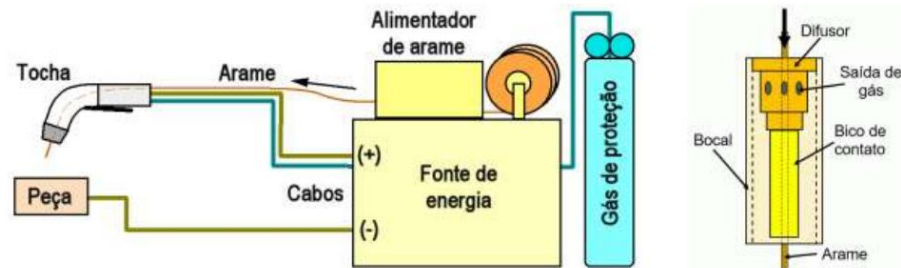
Equipamentos para Soldagem FCAW (Esquemática) - Fonte: Introdução aos Processos de Soldagem, Belo Horizonte, jan. 2022, Pág. 31.
